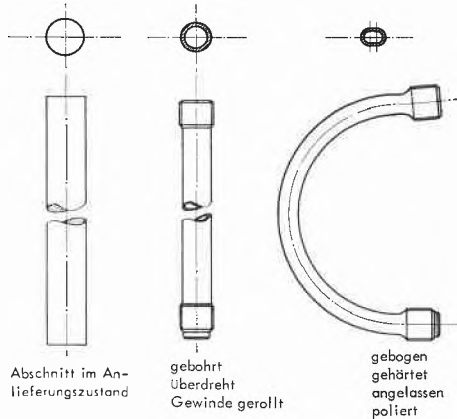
Die Bearbeitungsstufen einer Hydraulikfeder
